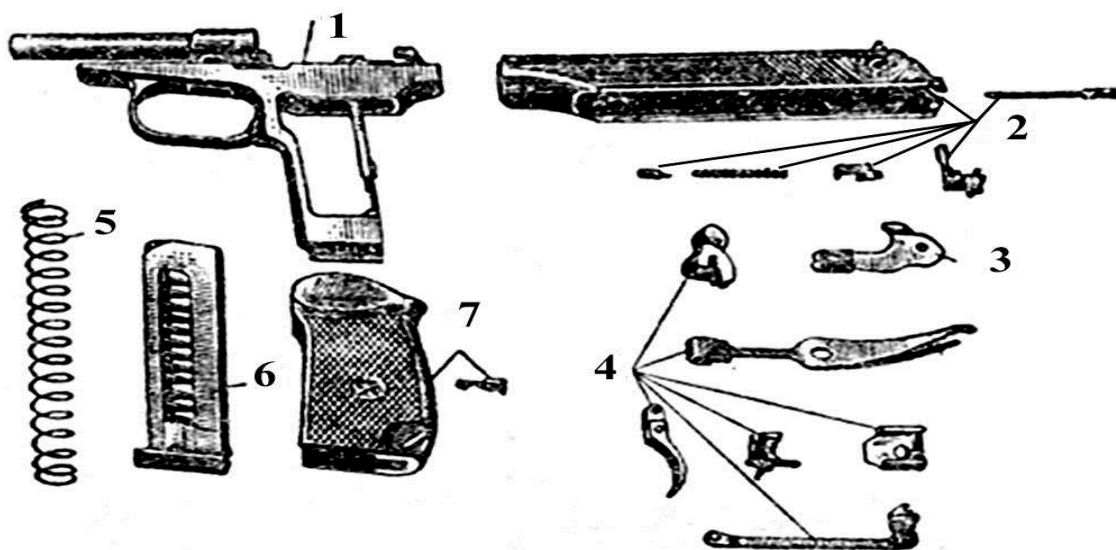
Основные части и механизмы: 1 — рамка со стволом и спусковой скобой; 2 — затвор с ударником, выбрасывателем и предохранителем; 3 — затворная задержка; 4 — ударно-спусковой механизм; 5 — возвратная пружина; 6 — магазин; 7 — рукоятка с винтом
